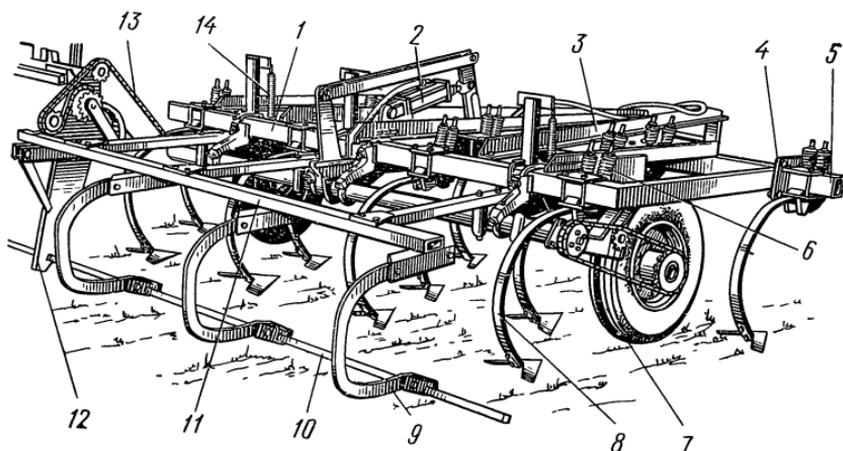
Культиватор КПЭ-3,8 со штанговым приспособлением:
